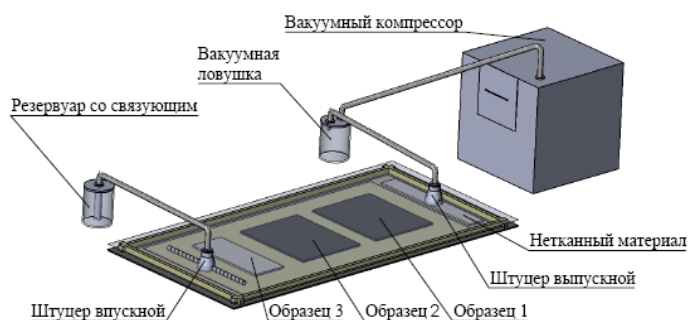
Устройства для изготовления листовых изделий методом вакуумной пропитки
